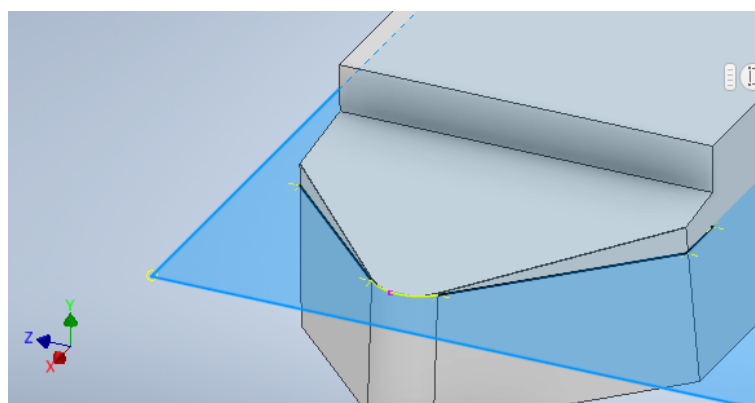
Criação do Plano Auxiliar 1, ou Plano de Referência
